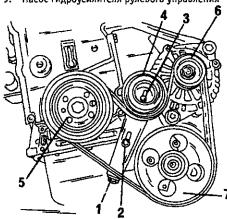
Натяжение приводного ремня при устройстве натяжения ремня с ручной регулировкой (двигатели типа XU).
